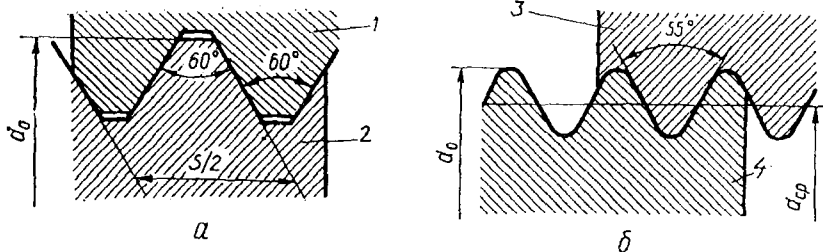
Профиль треугольной резьбы: а – метрическая резьба; б – трубная резьба; 1 – гайка; 2 – болт; 3 – муфта; 4 – труба.
